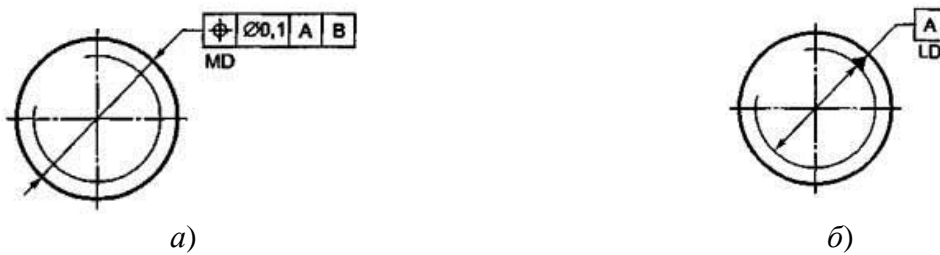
Обозначение допусков и баз с дополнительными знаками
